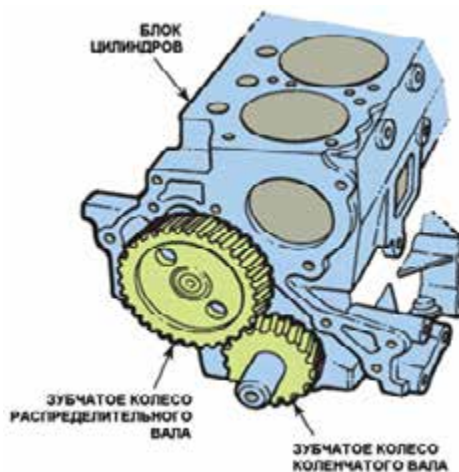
Крупные шестерни распределительных валов обычно изготавливаются из стекловолокна, и наделены спиральными нарезными зубьями, чтобы помочь уменьшить шум. Шестерня распределительного вала в два раза больше шестерни коленчатого вала, что позволяет поворачиваться распределительному валу на один оборот за каждые два оборота коленчатого вала; источник: *Pearson Education, Inc.
